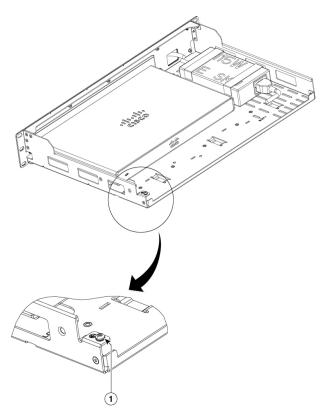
Option de mise à la terre sur la face avant du plateau
